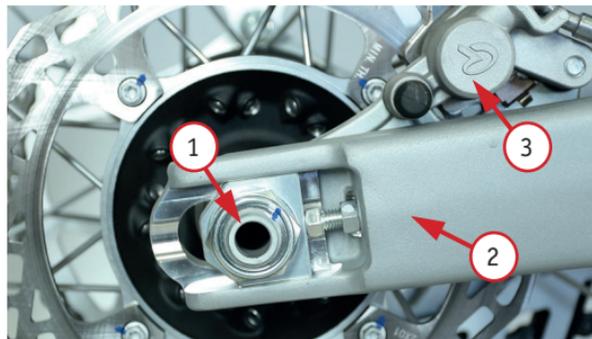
Снятие заднего колеса: 1 – ось колеса; 2 – маятник; 3 – задний тормозной суппорт
